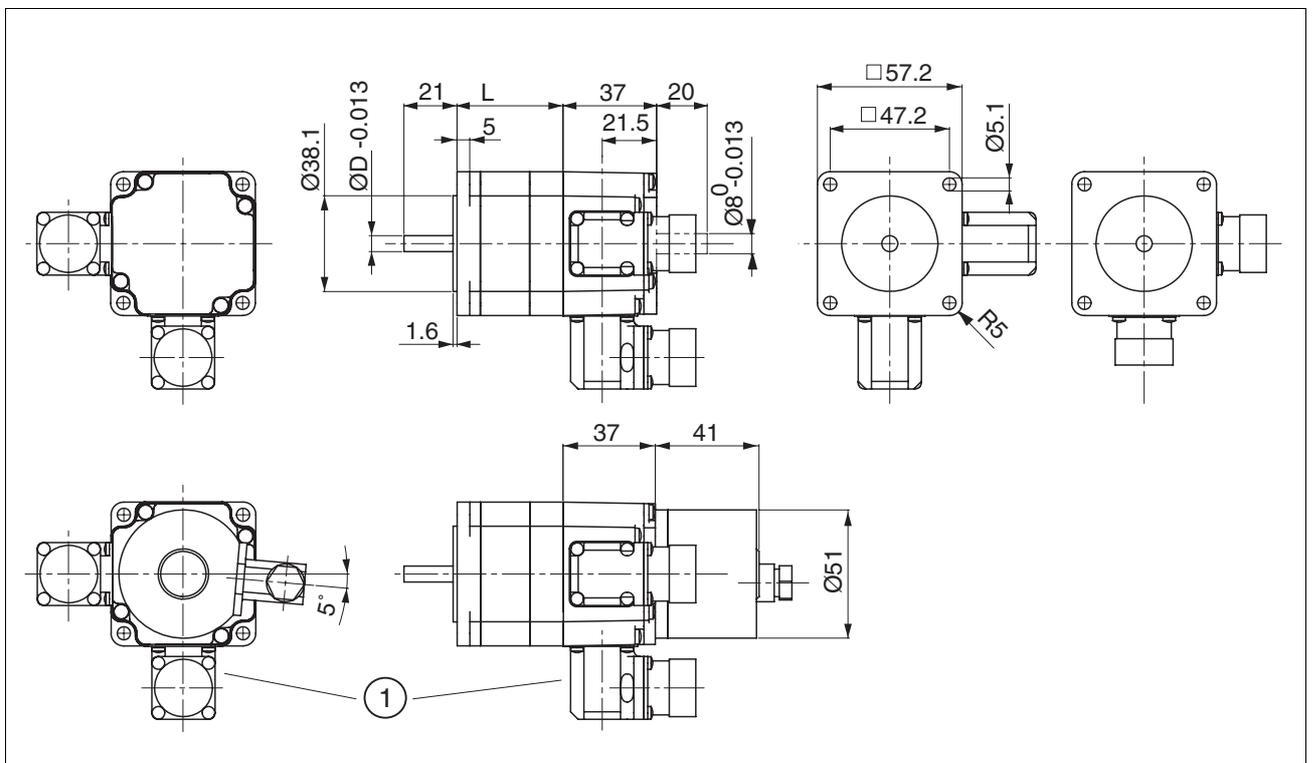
BRS36 Maßzeichnung Steckerausführung mit Encoder
